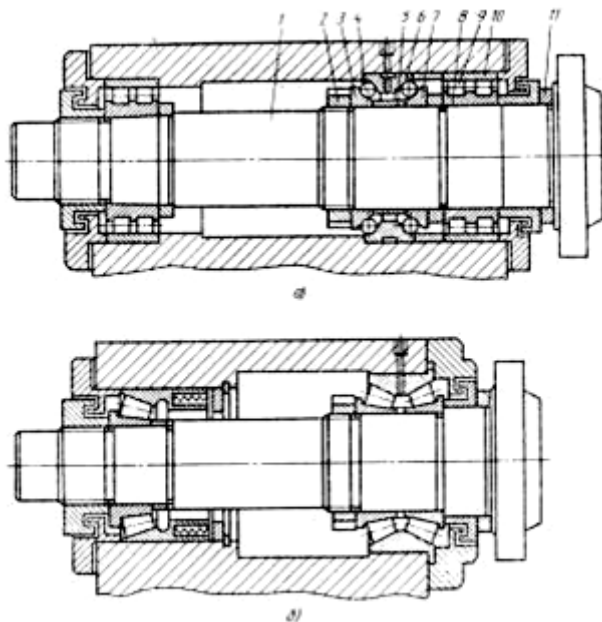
Конструкция передней опоры шпиндельного узла станка с ЧПУ
